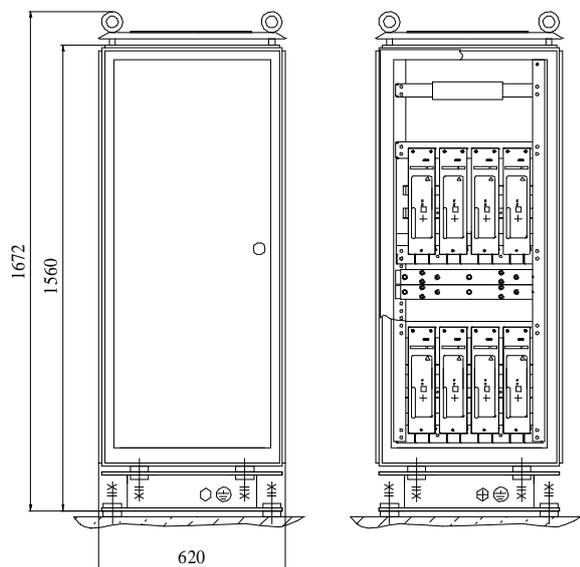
Габаритный чертёж СУЭП-3-У (глубина стойки 620мм)
